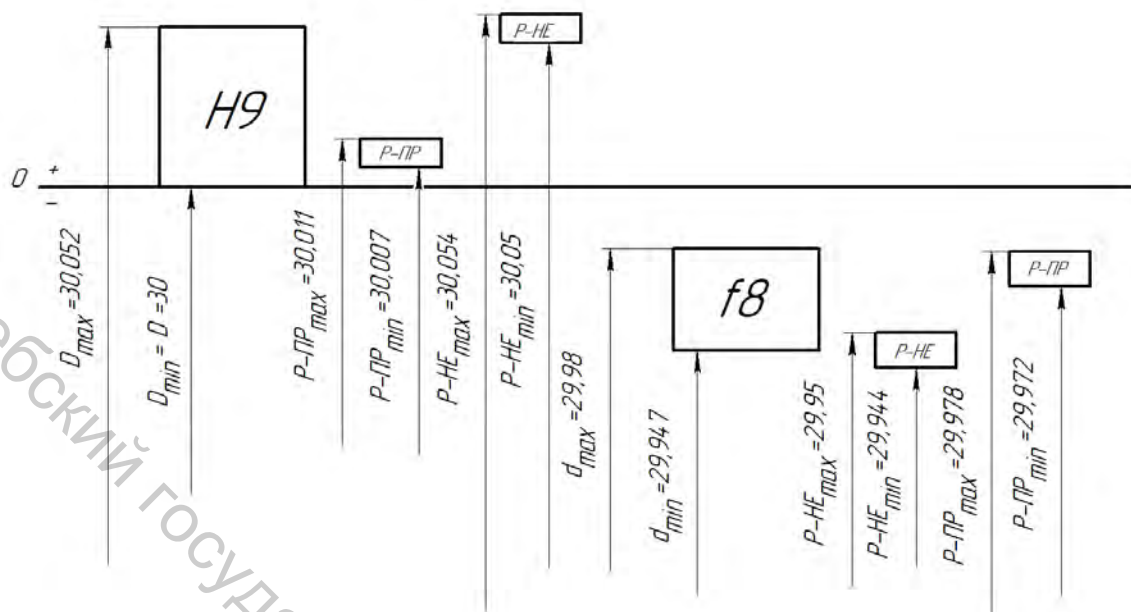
Схема расположения интервалов допусков отверстия, вала и рабочих калибров для посадки  $\varnothing 30 \frac{H9}{f8}$
